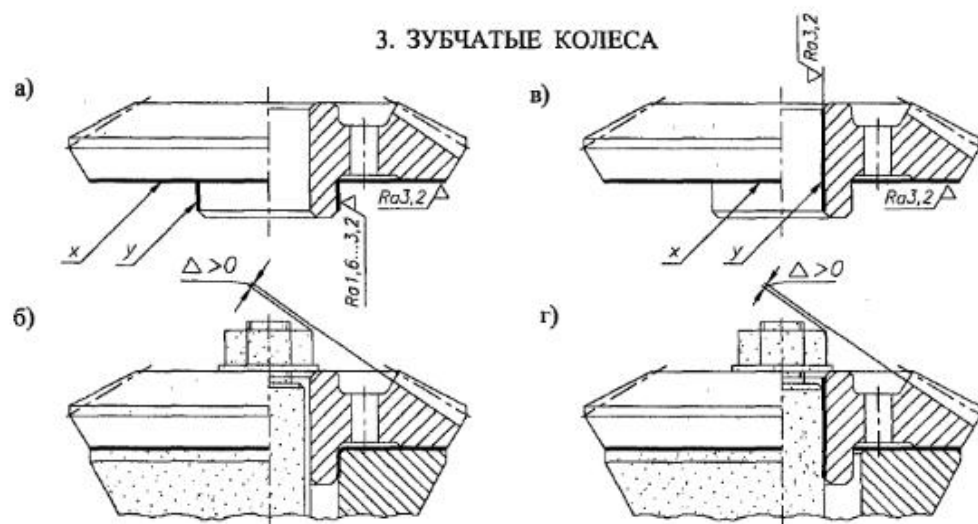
Установочные базы для нарезания зубьев на зубчатых колесах
